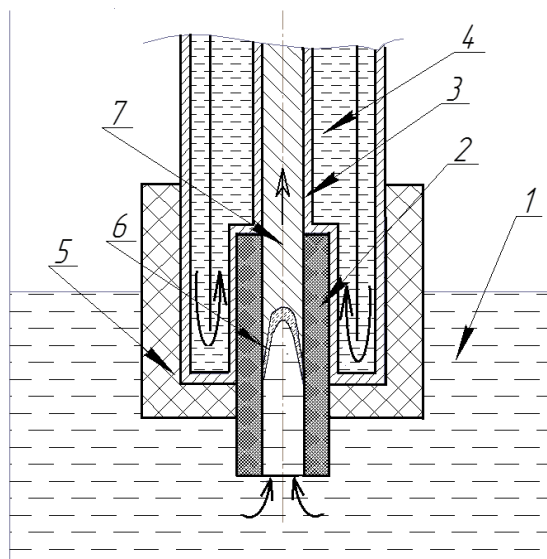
Принципиальная схема нижней части кристаллизатора, погруженной в расплав: 1 – расплав; 2 – графитовая рубашка; 3 – медный корпус; 4 – охлаждающая вода; 5 – огнеупорный чехол; 6 – лунка слитка; 7 – сформировавшаяся заготовка.
